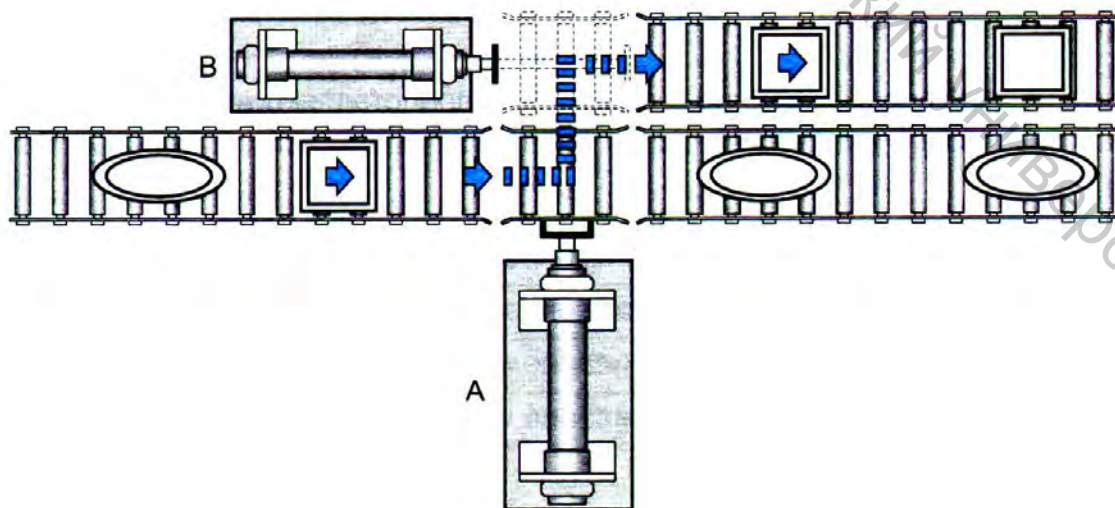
Эскиз установки для перемещения заготовок
